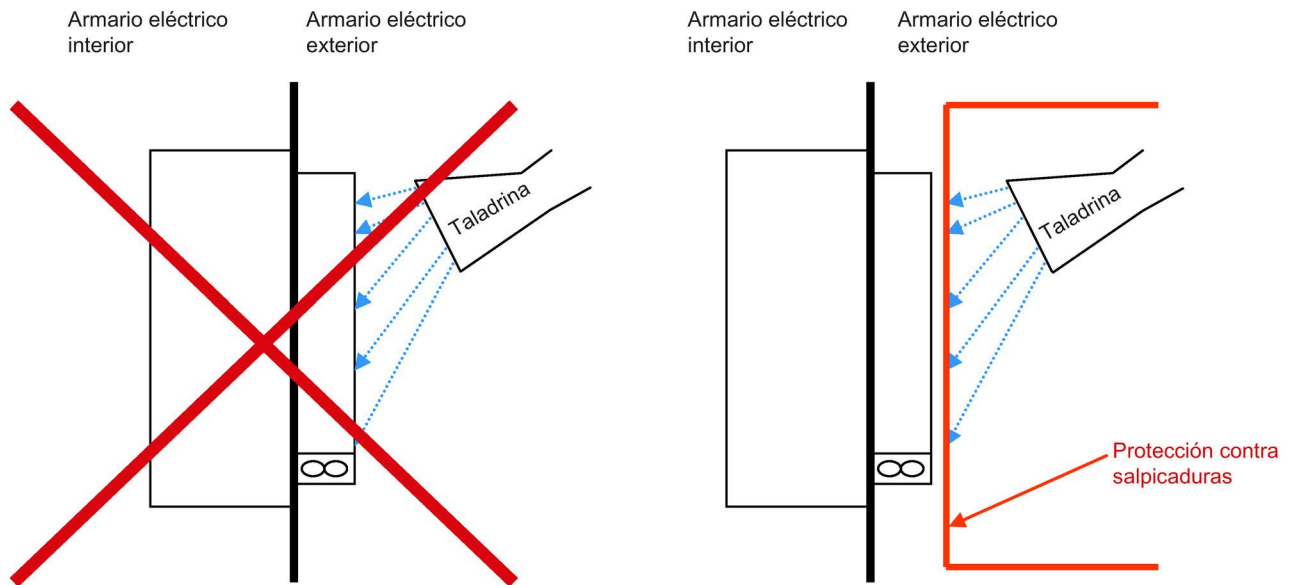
Protección contra salpicaduras en un grupo de accionamientos con refrigeración por aire externa
